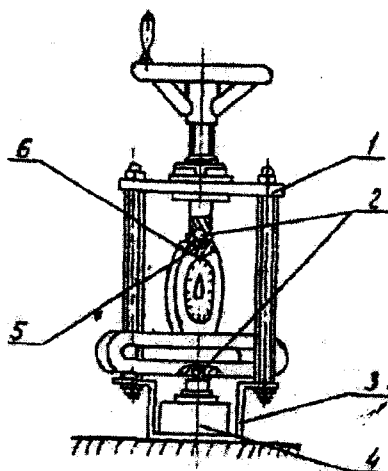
Схема приспособления и монтажа силоизмерительного устройства:
